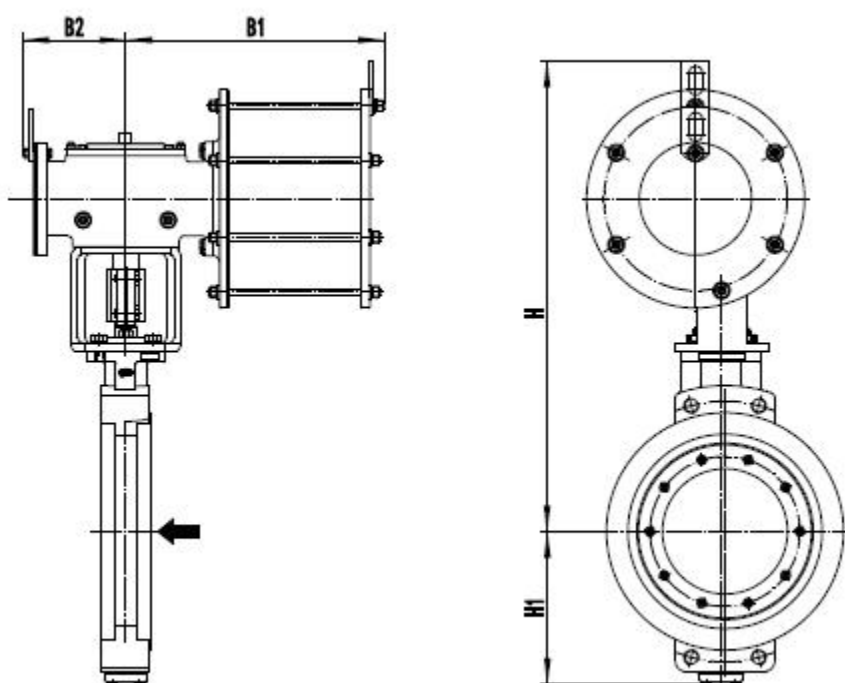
配 AW18D001~AW40D004 外形尺寸图
